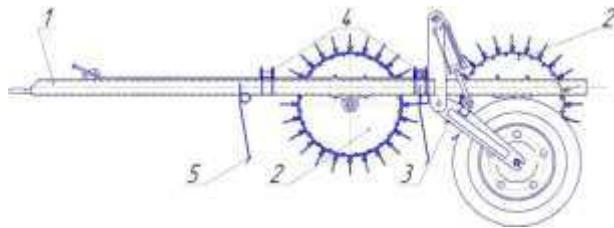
Схема катка-измельчителя растительных остатков: 1 - рама с прицепным устройством; 2 - катки с ножами; 3 - гидравлический механизм транспортного положения; 4 - гидравлические цилиндры подъема боковых катков; 5 - пружинные пальцы-направляющие
